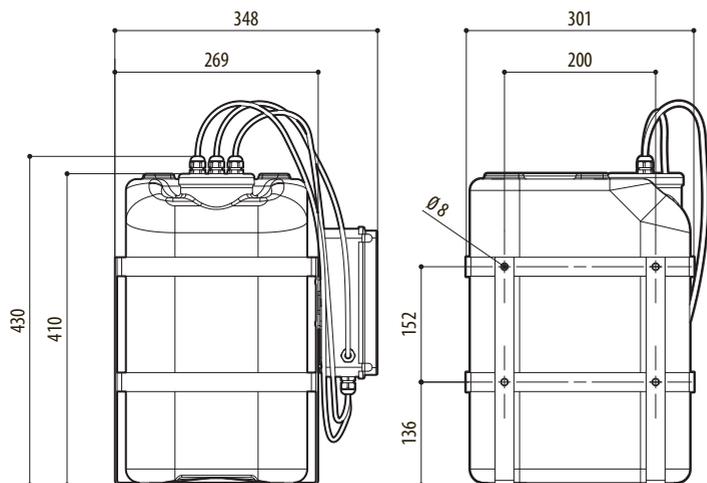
Réservoir 23l, hauteur de remontée d'eau de 11m.
